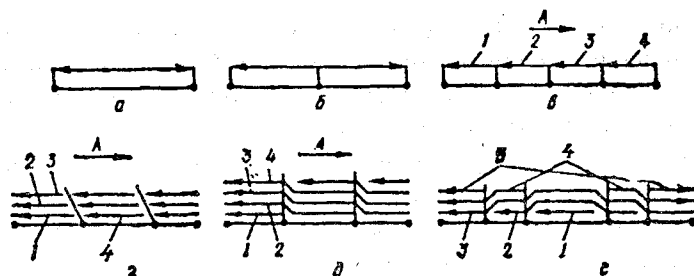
Схемы сварки: а — на проход; б — от середины к краям; в — обратноступенчатым способом; г — блоками; д — каскадом; е — горкой; А — направление заполнения разделки; 1—5 — последовательность сварки в каждом слое
